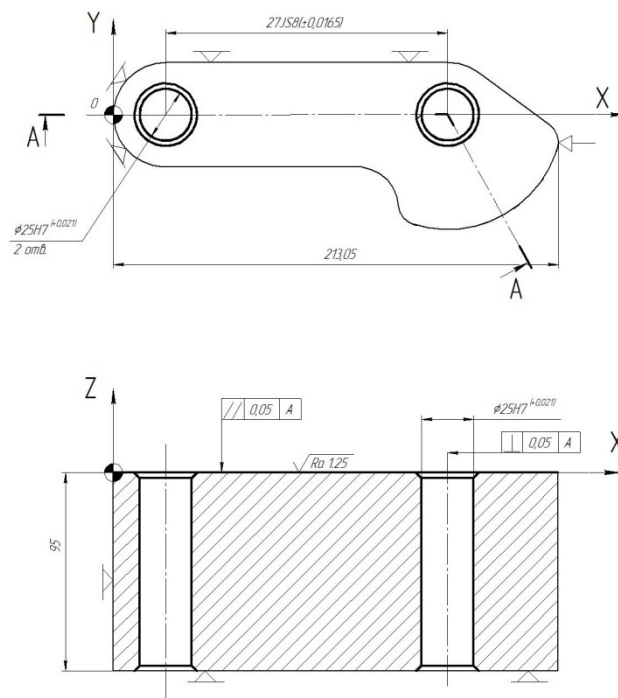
Схема базування заготовки на фрезерній операції
